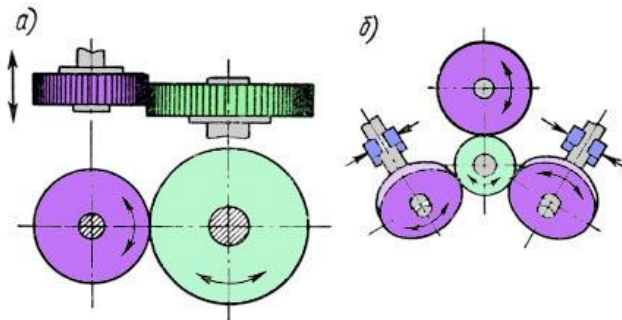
Схема притирання зубів циліндричних зубчастих коліс
